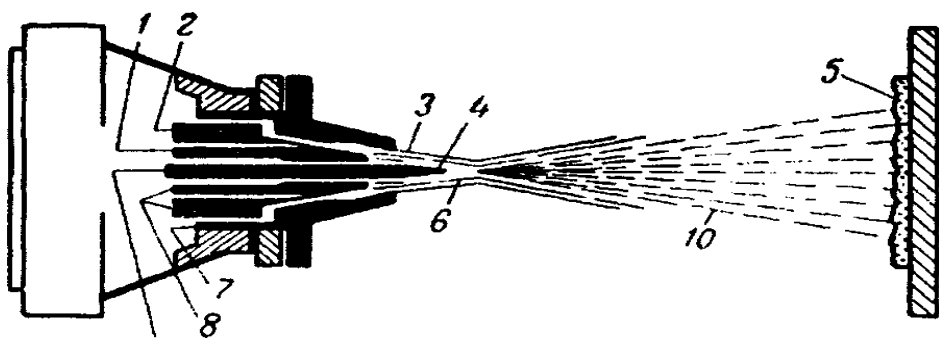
Принципиальная схема металлизации газопламенным проволоочным аппаратом: 1 — кислород-ацетилен; 2 — сжатый воздух; 3 — кислородно-ацетиленовое пламя; 4 — плавление проволоки; 5 — напыленный металл; 6 — горючий газ; 7 — воздушные отверстия; 8 — газовые отверстия; 9 — проволока; 10 — распыленный металл
